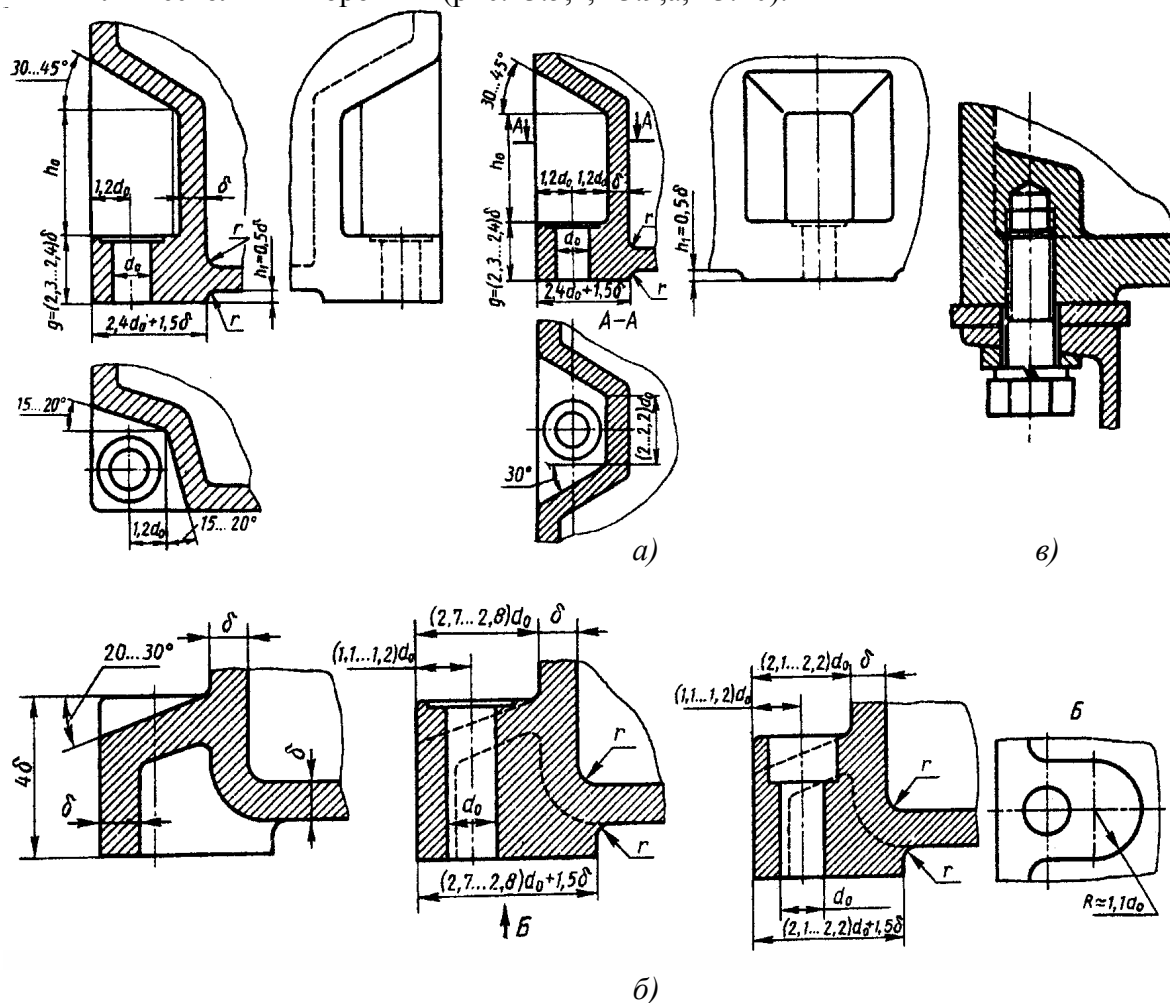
Опорные фланцы крепления корпусов к основанию
